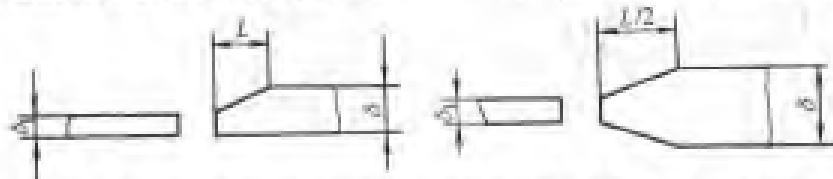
气焊、手工电弧焊、气体保护焊坡口基本形式和尺寸
